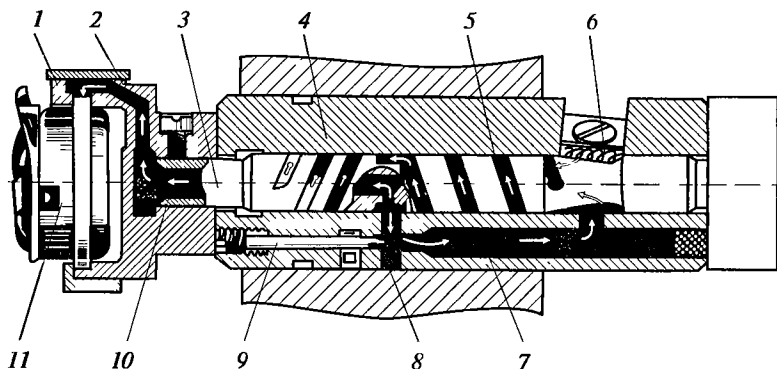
Схема системы смазывания деталей в механизме челнока швейной машины класса 1022М
